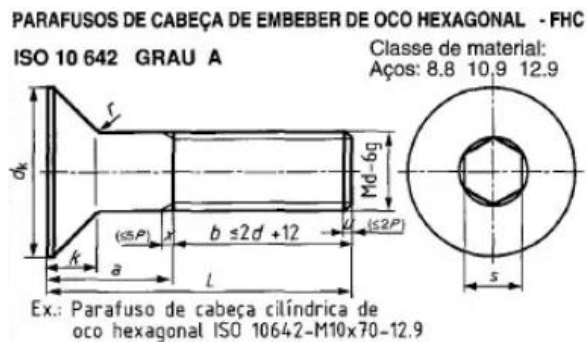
Desenho técnico de parafusos de cabeça de embeber de oco hexagonal
